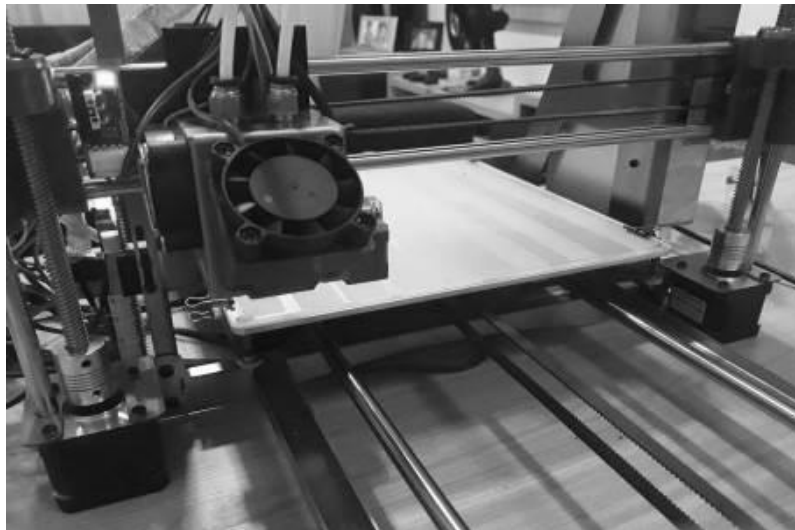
Impressora 3D *Zonestar Diy 802QR2* com a técnica de Modelagem por Fusão de Deposição - FDM
